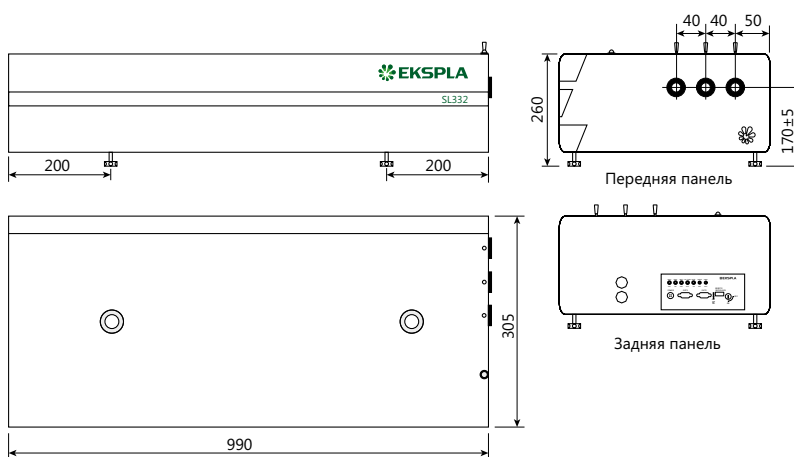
Габаритные размеры лазеров SL332, SL333 и SL334
